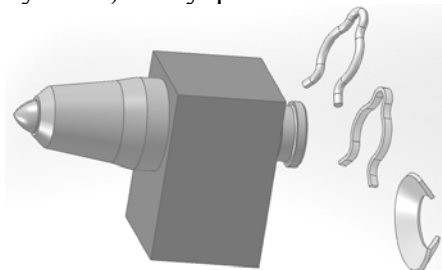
Внешнее закрепление ТПР в резцедержателе с помощью стопоров различной конструкции
